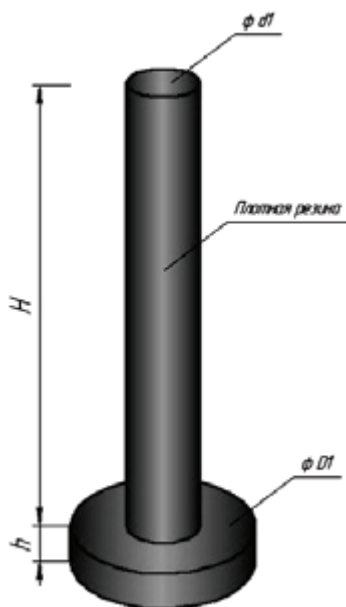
Деталь 1 – цилиндрический стержень и цилиндрическое основание из плотной резины.
